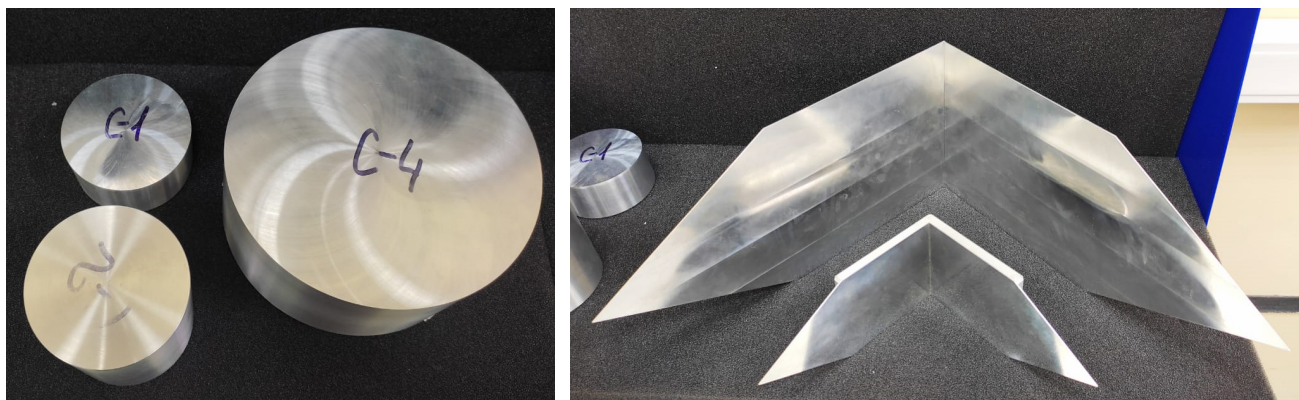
Общий вид отражателей эталонных Цилиндр 100, Цилиндр 200, Цилиндр 400, Отражатель уголкового 100, Отражатель уголкового 200
